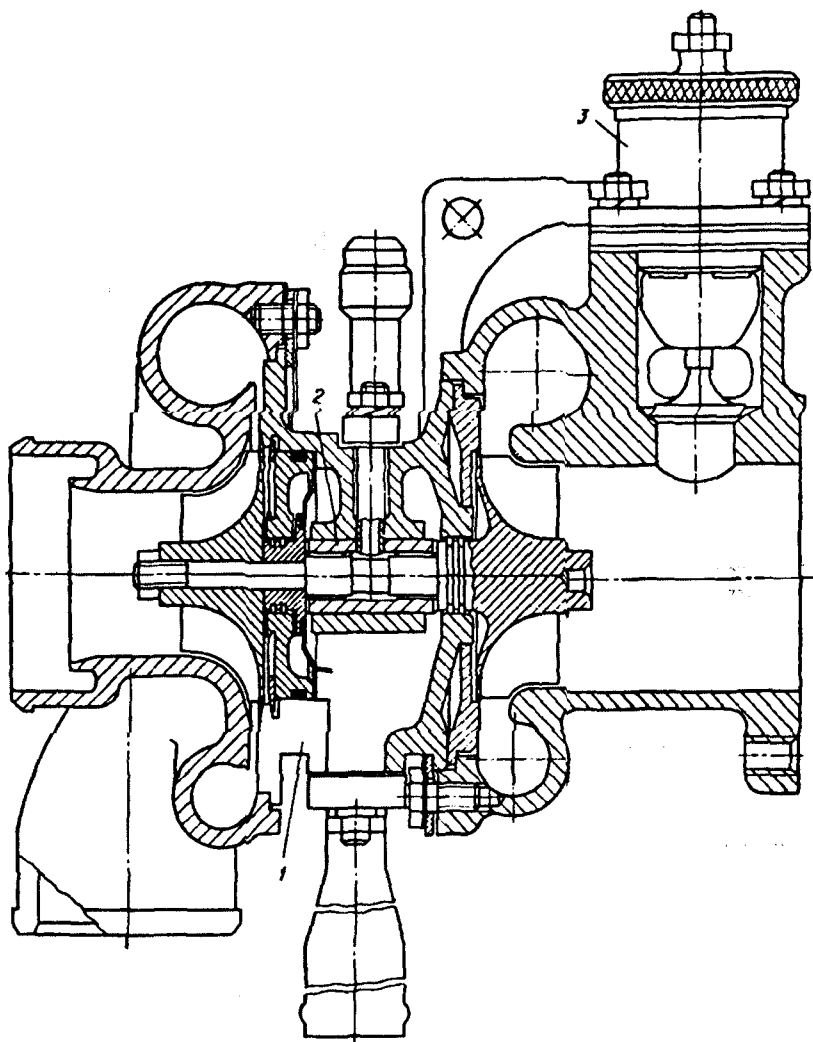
Турбокомпрессор типоразмера ТКР 5,5:
